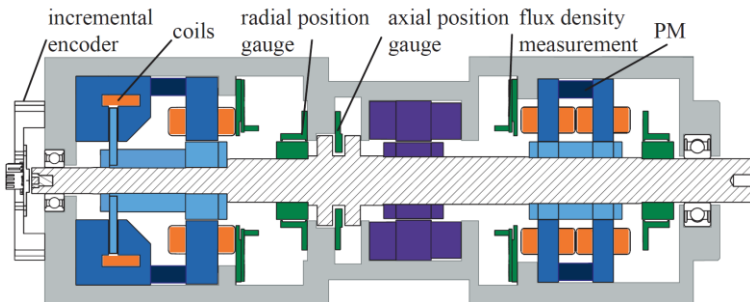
Versuchsaufbau mit Kombilager (links) und Unipolarlager (rechts). Test rig with combined radial/thrust bearing (left) and hybrid bearing (right)
